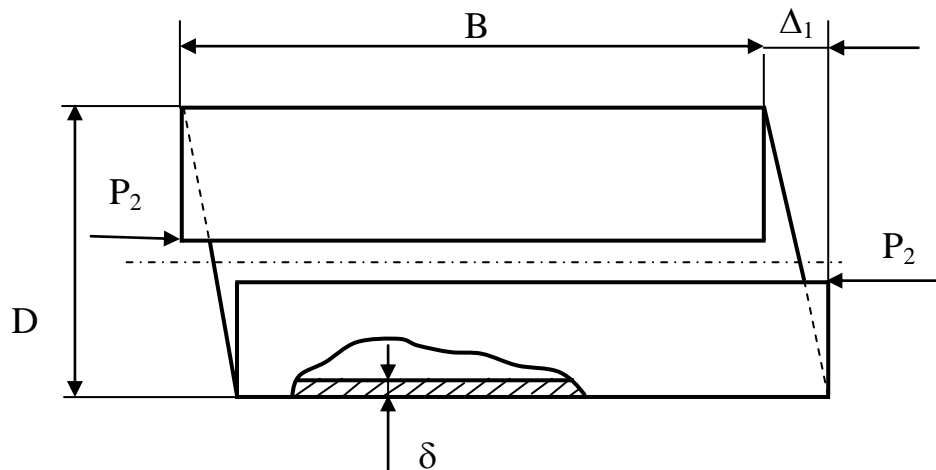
Розрахункова схема визначення величини сили для вирівнювання торців циліндричної обичайки
